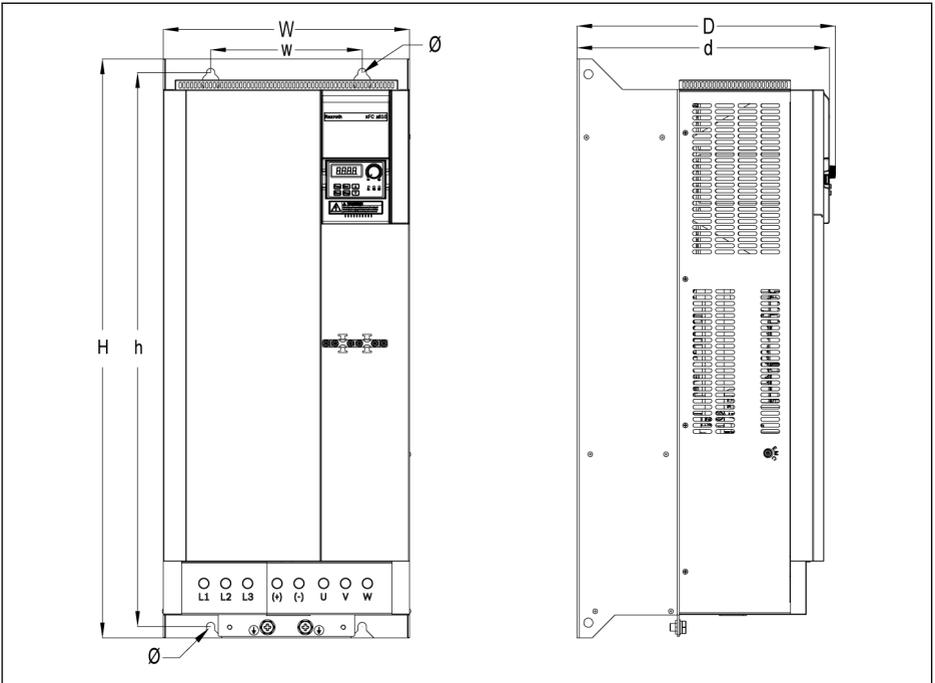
EFC 5610 75K0...90K0 Maßzeichnung
